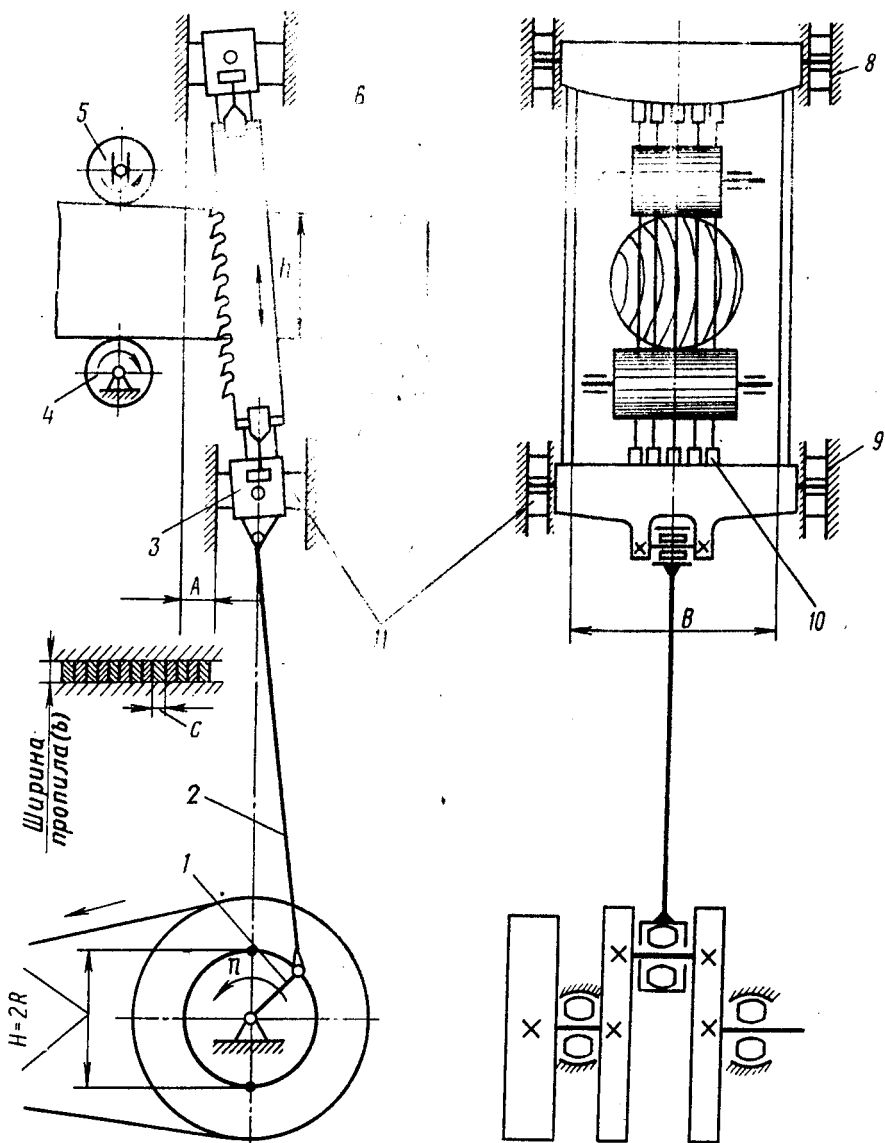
Принципиальная схема двухэтажной лесопильной рамы:
